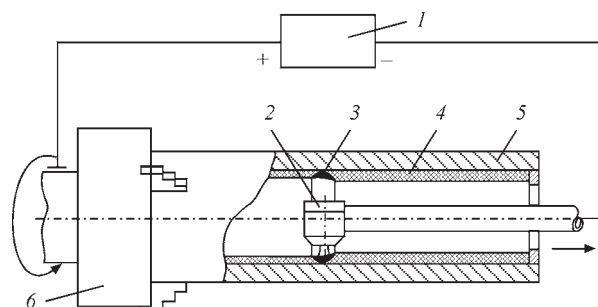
Схема ЦПН: 1 – джерело живлення; 2 – плазмотрон; 3 – кільцева зварювальна ванна; 4 – присадний порошок; 5 – деталь; 6 – токарний патрон
